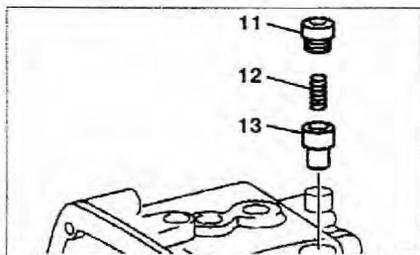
Ослабьте и открутите пробку 11. Снимите пружину 12 и упорную деталь 13 из корпуса коробки передач.
